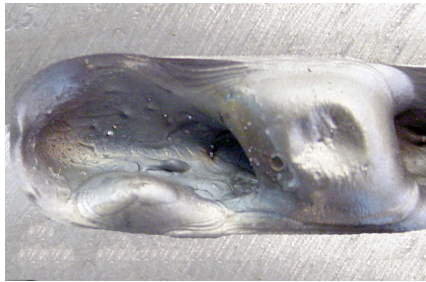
Detalhe da cratera que se forma durante a soldagem.
